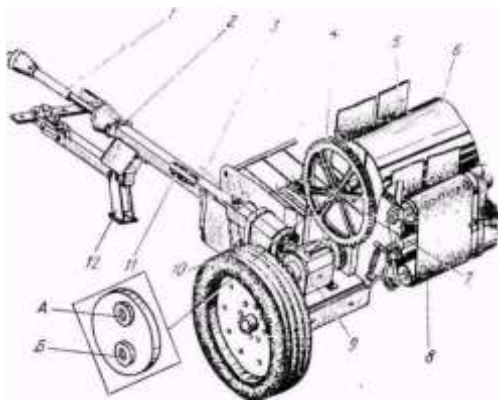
Сница с карданной передачей: 1 - вал карданный; 2 - опора; 3 - сница; 4 - колесо зубчатое; 5 - ремень прессующий; 6 - барабан; 7 - эксцентрик; 8 - транспортер; 9 - редутор; 10 - кожух муфты; 11 - вал промежуточный; 12 - опора сницы. А и В - отверстия эксцентрика
